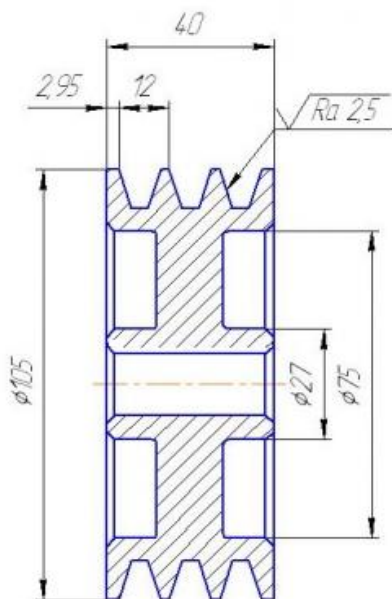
Чертеж «Ведущий шкив поликлиновой ременной передачи»
